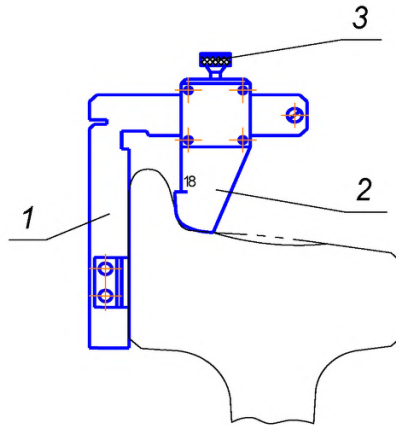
Контроль вертикального подреза гребня колеса
